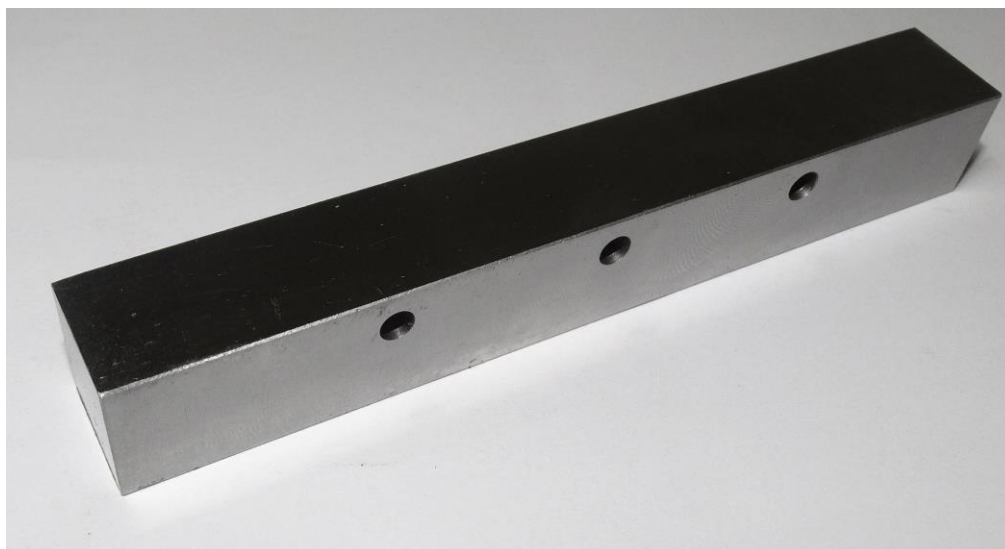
Corpo de prova confeccionado no aço AISI H13 com três furos para inserção dos termopares
